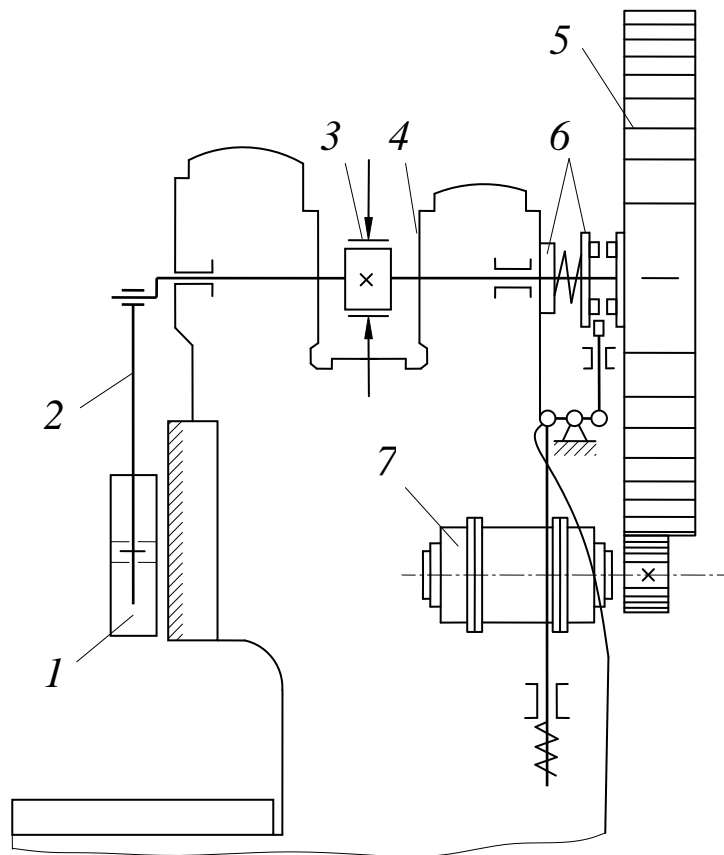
Схема кривошипно-ексцентрикового преса
